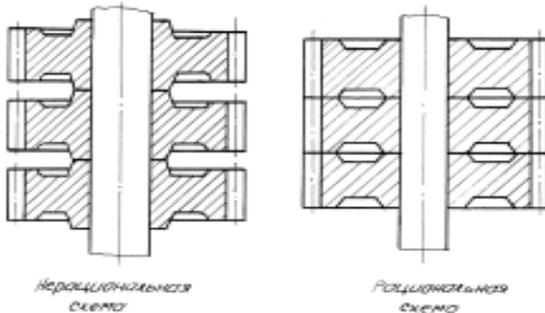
Различные схемы установки заготовок для их одновременной обработки
